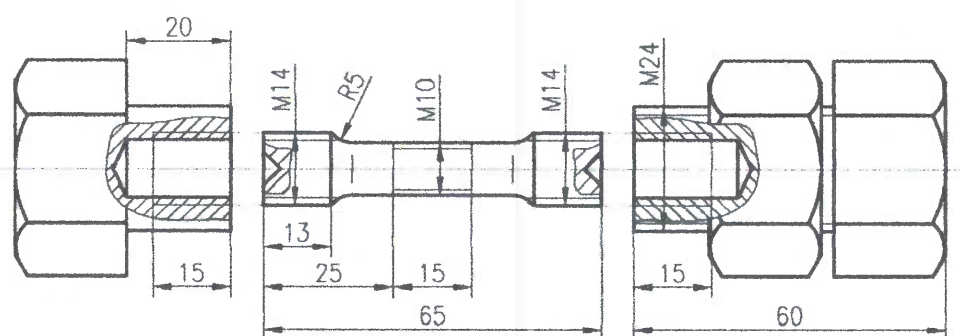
конструкция образца с резьбой М10 и захватные приспособления для испытаний
